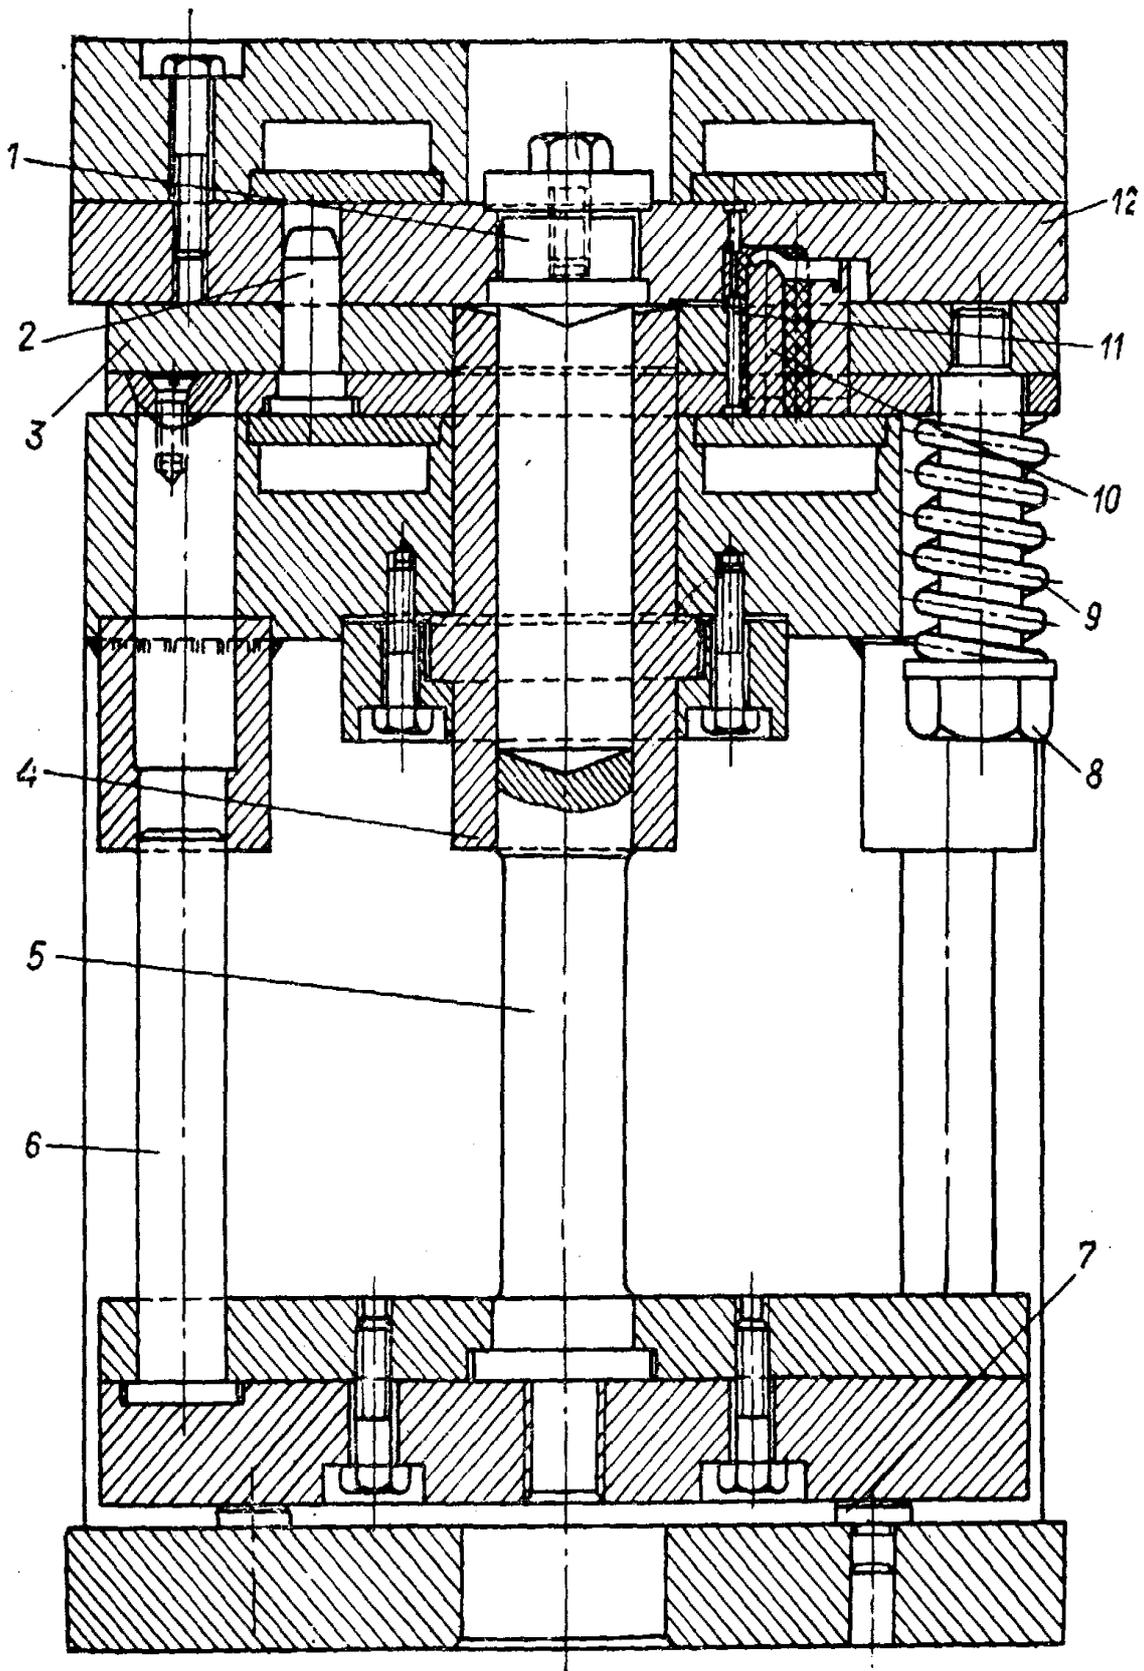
Общий вид стационарной многогнездной пресс - формы для литейного прессования.
